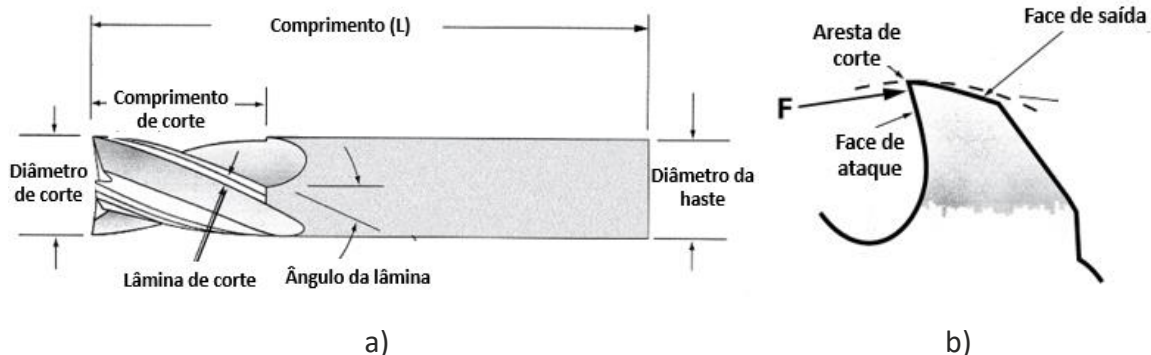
Legenda geométrica – a) fresa monobloco b) detalhe ferramenta (adaptado de [28])
